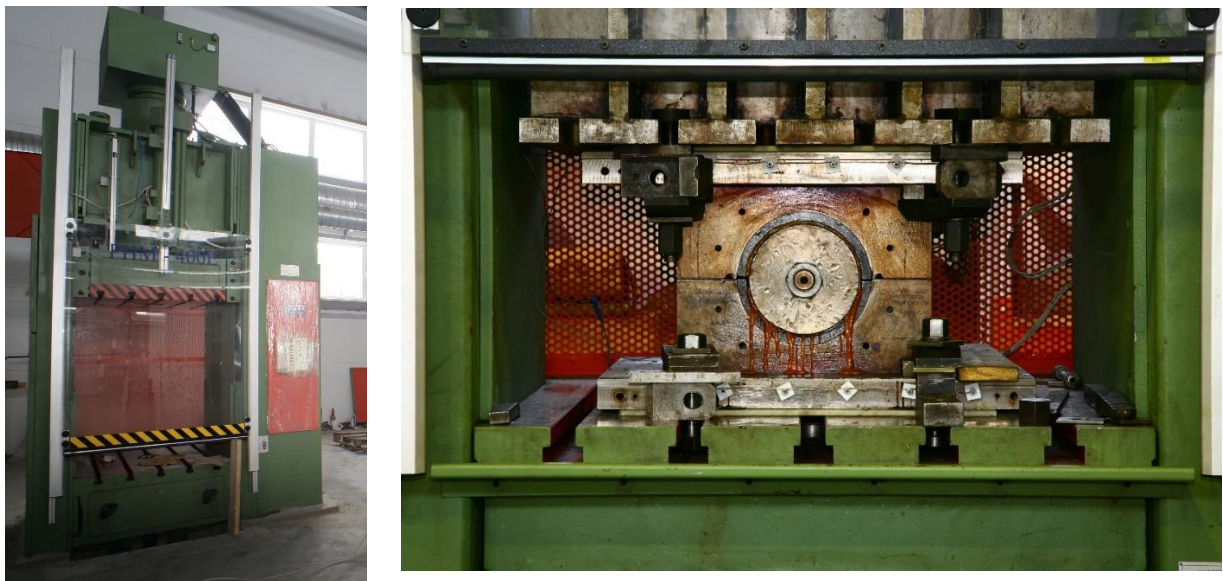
а) Внешний вид пресса РНМ-250; б) процесс прессования.
